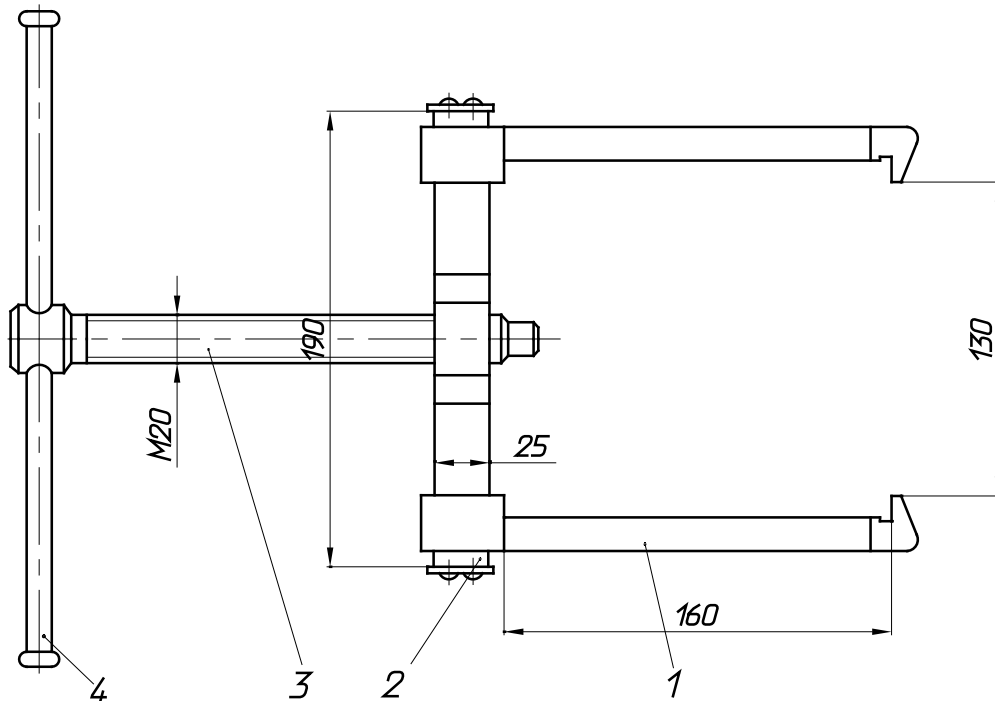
Съемник противовеса и шестерни коленчатого вала
